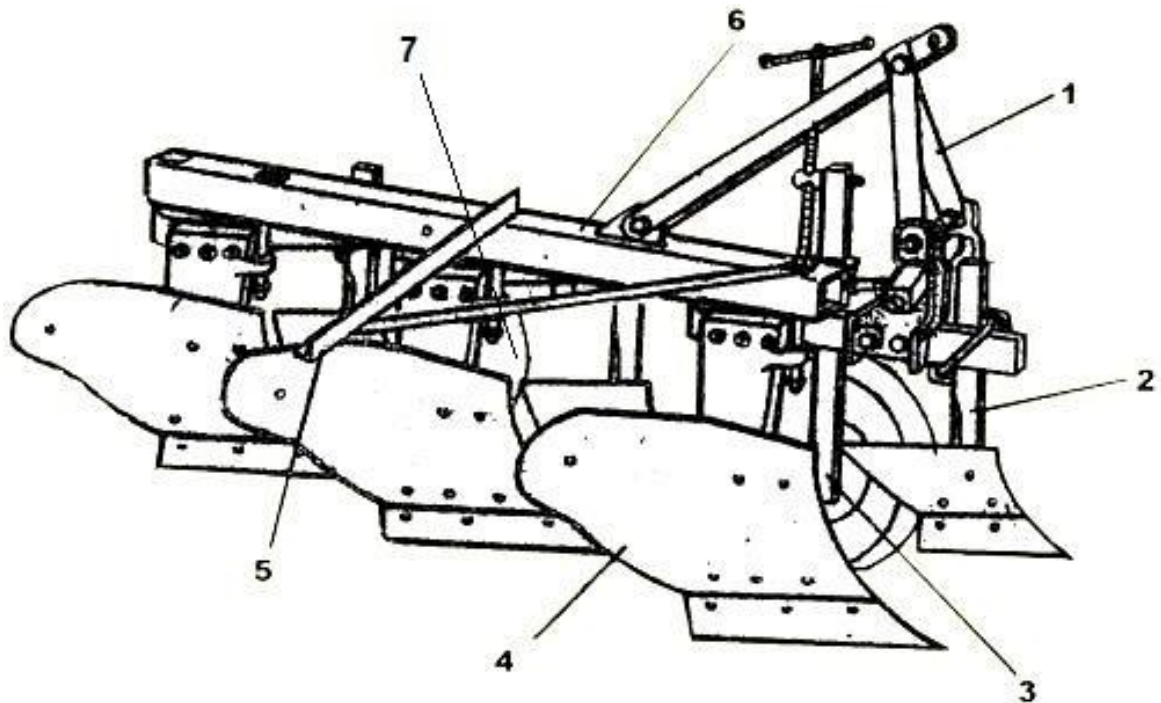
Плуг трикорпусний начіпний ПЛН-3-35
